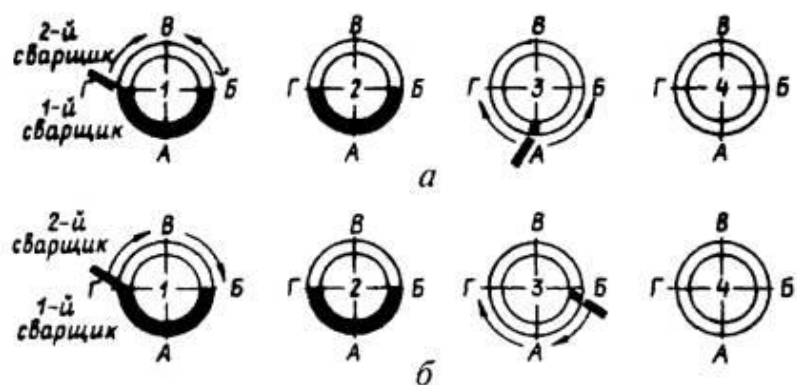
Порядок сварки двумя сварщиками вертикальных (а) и горизонтальных (б) стыков.
